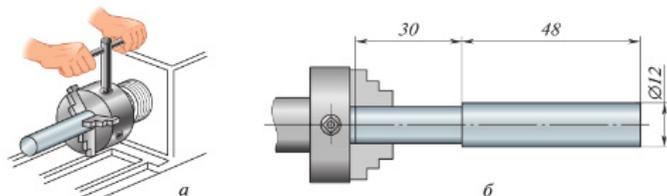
Закрепление заготовки в патроне токарного станка:
